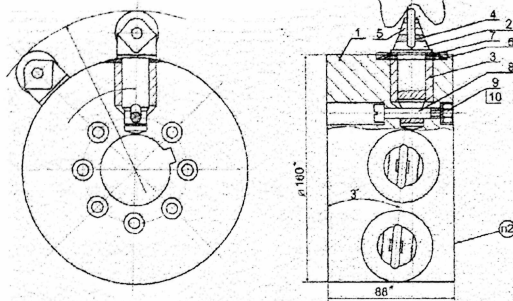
Инструмент для обработки объемным пластическим деформированием выкружки зубчатых колес среднего модуля
